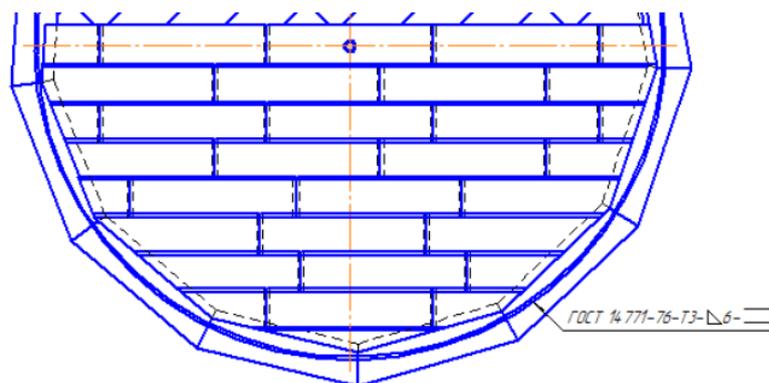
Сварка по дуговому контуру днища с окрайкой
